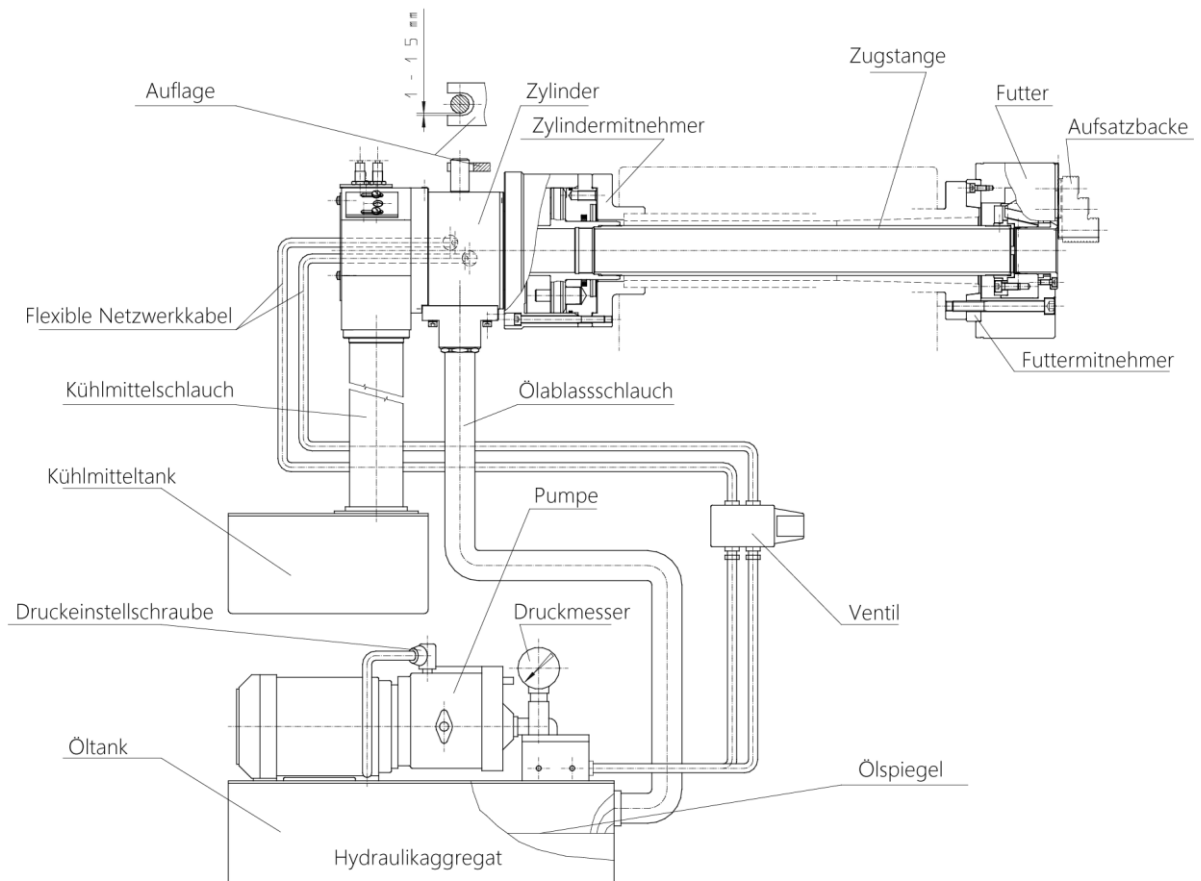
Einbau eines mechanischen Spannfeeders mit Durchgang
